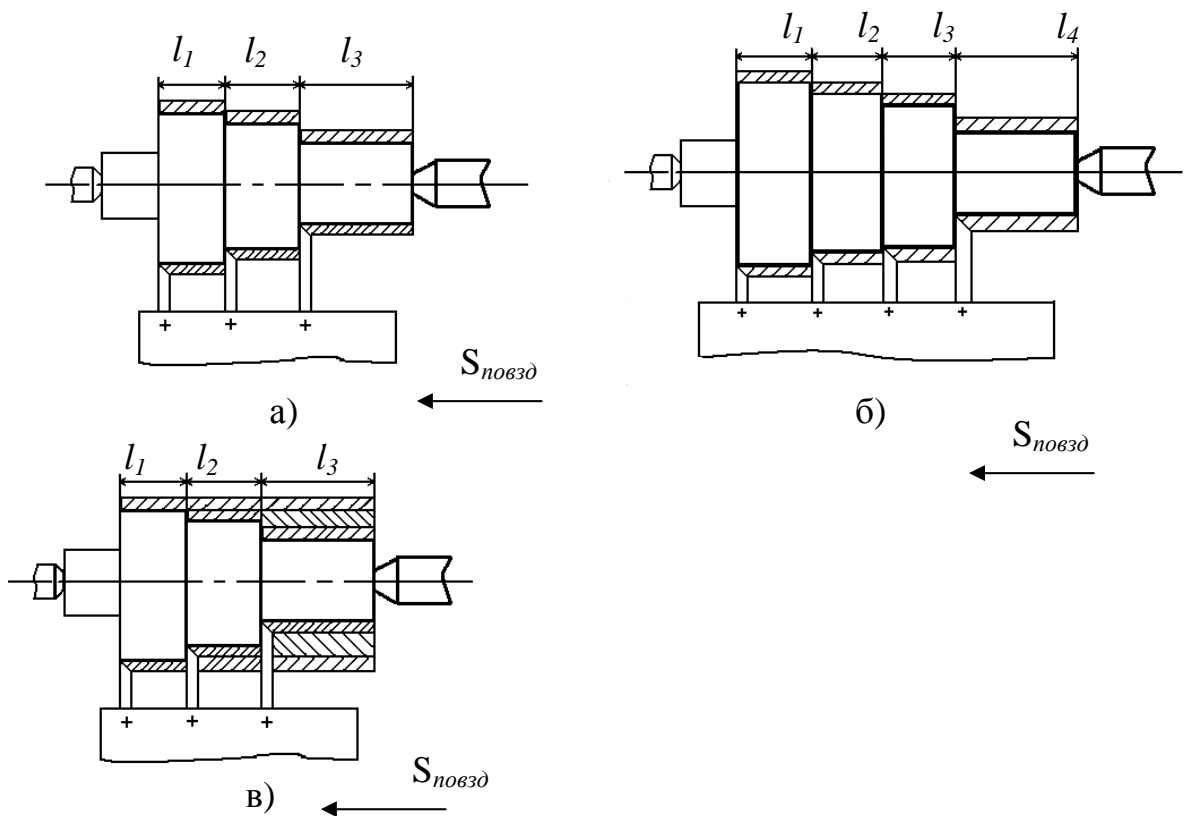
Три схеми обточування поверхонь валів на багаторізцевих верстатах
